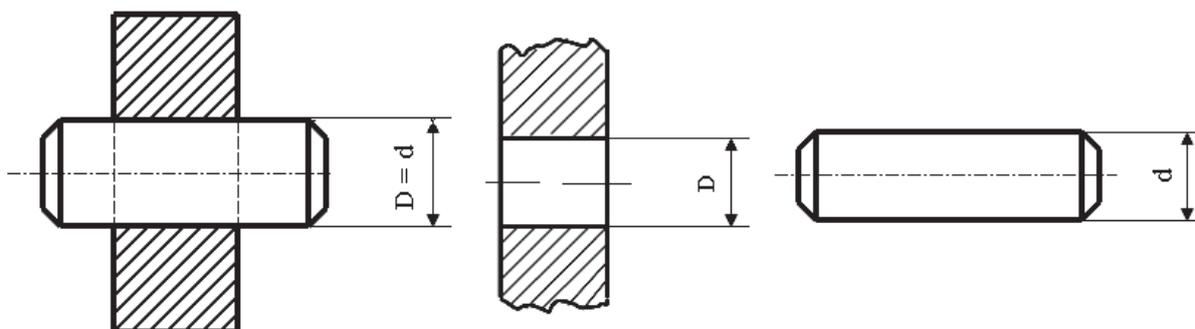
Гладкое цилиндрическое соединение и его детали
